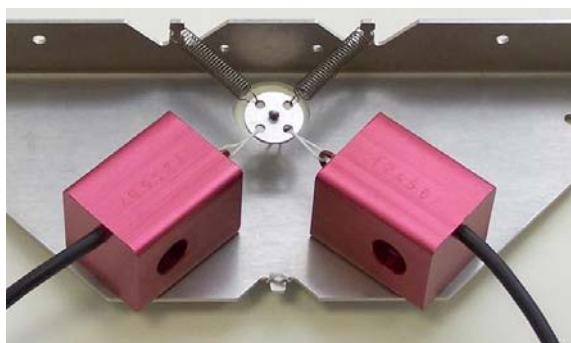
Fixação dos sensores de força no grupo de montagem de molas
